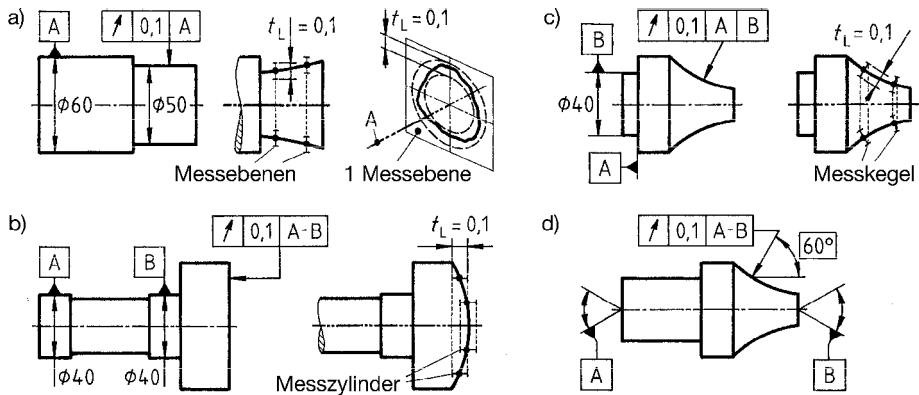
Lauftolerierung. a) Rundlauf eines Wellenzapfens, mit kreisringförmigen Toleranzzonen; b) Planlauf einer Stirnfläche, mit zylinderförmigen Toleranzzonen; c) Lauf in beliebiger Richtung, mit kegelförmigen Toleranzzonen; d) Lauf in festgelegter Richtung (entsprechend c)
